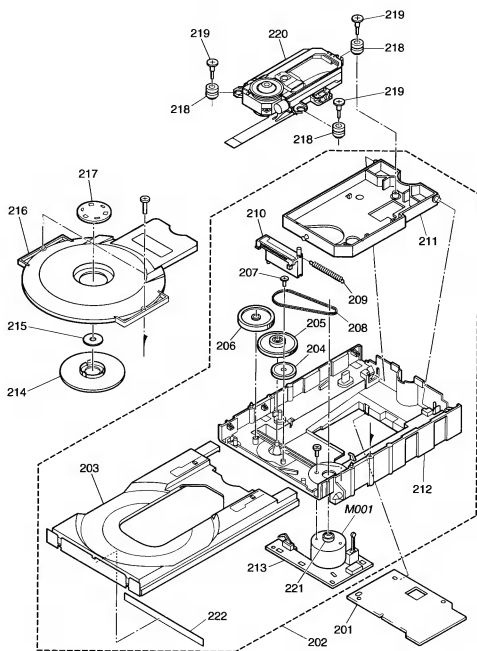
Сборочный чертеж механизма привода дисков и устройства загрузки дисков моделей условного типа 1
